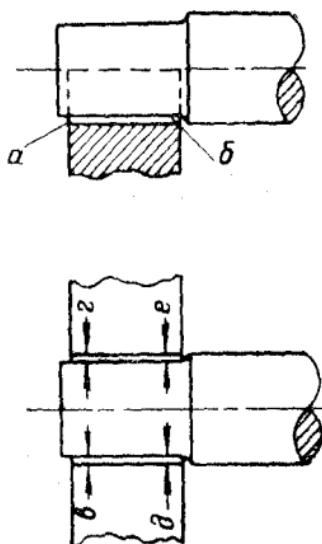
Схема проверки зазоров между шейкой вала и вкладышем подшипника
